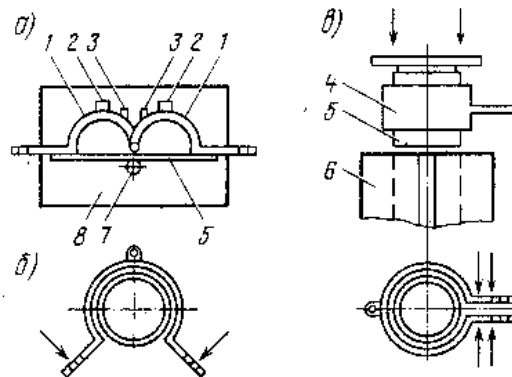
Захват для предварительного свертывания пластин и ввода их в пресс-форму: а — размещение захвата и пластины на плите в исходном положении; б — схема свертывания пластины; в — ввод предварительно свернутой пластины в пресс-форму; 1 — левое полукольцо захвата; 2 — упоры полуколец; 3 — упоры полуколец захвата; 4 — первое полукольцо захвата; 5 — пластина; 6 — пресс-форма для свертывания пластины в цилиндр; 7 — цилиндрический стержень-упор; 8 — плита
